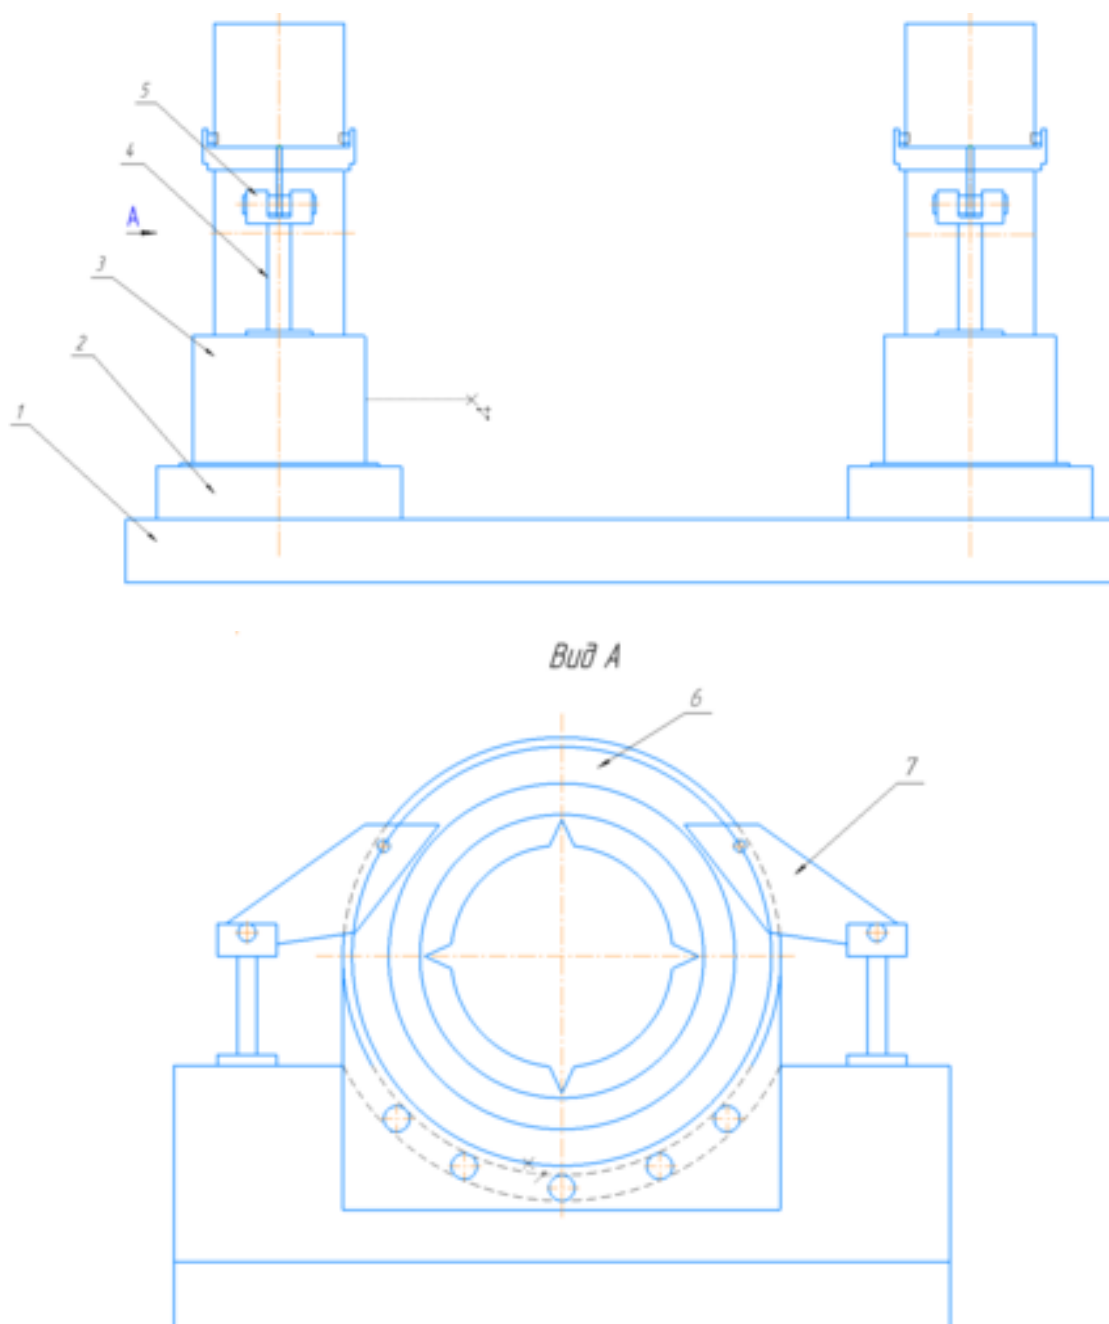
Общий вид кольцевого кантователя. Состоящего из: 1- плита опорная; 2 – основание; 3 – гидроцилиндр; 4 – шток гидроцилиндра; 5 – вилка; 6 – Прижим подвижный; 7 – кулак
